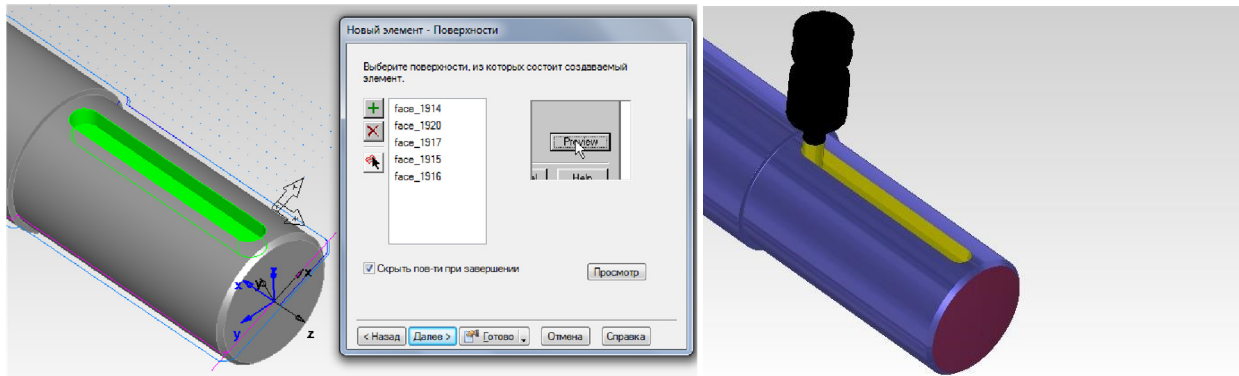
Вибір поверхонь для операції фрезерування пазу
